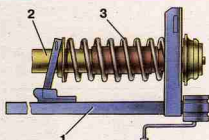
Разборка стойки передней подвески: 1 – приспособление 67.7823.9545; 2 – телескопическая стойка; 3 – пружина
